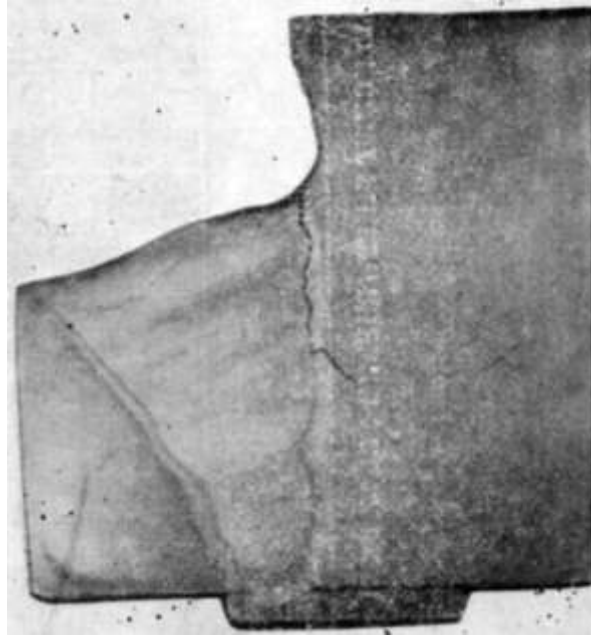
«Локальное» разрушение в околошовной зоне сварного соединения
